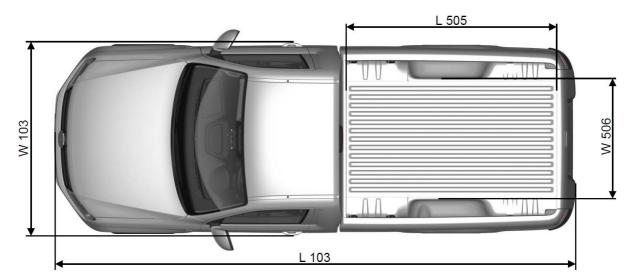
Vista dall'alto Amarok SC (Single Cab)
